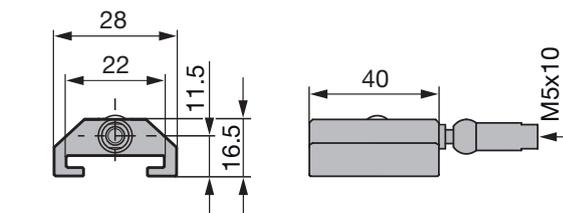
Medidas de montaje del sensor de posición BTL5-T-2814-1S
